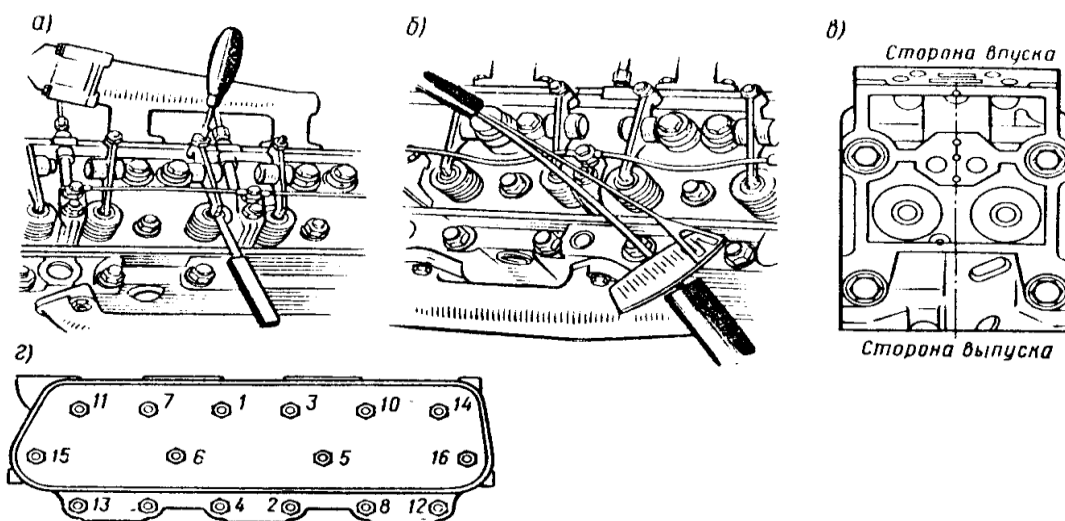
Проверка зазоров в клапанах и креплениях головки цилиндров двигателей;
